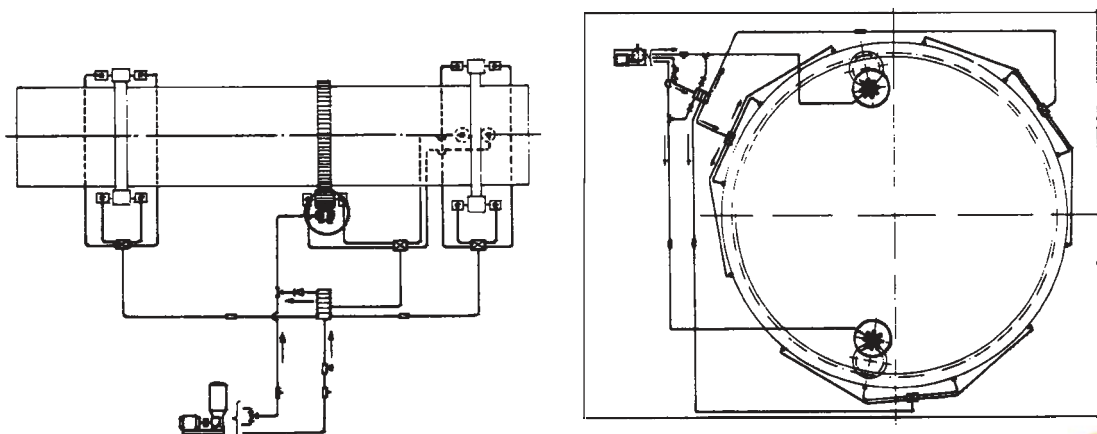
Вращающаяся печь, смазка шестерен и подшипников Рис. 16 Зубчатое колесо, комбинированная смазка
